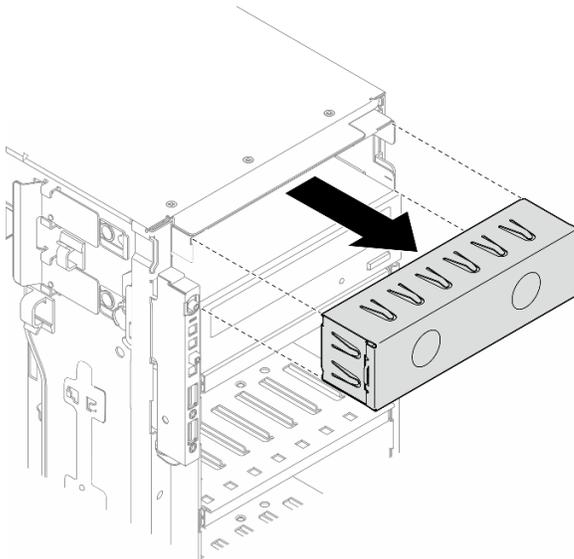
Entfernen der Abdeckblende für die Laufwerkposition
